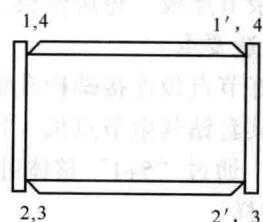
钢箱件棱角焊缝焊接次序示意图
